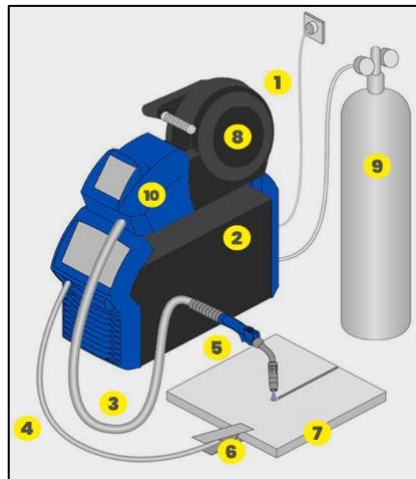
Equipos básicos de soldadura MIG.
